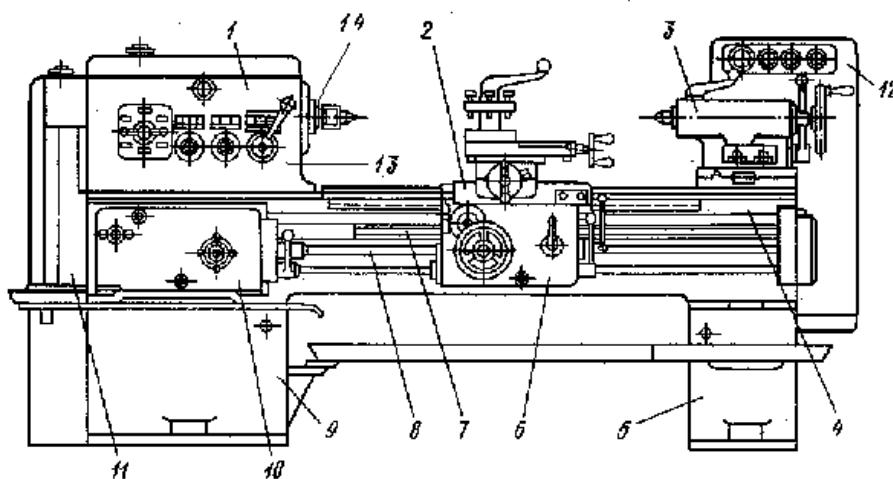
Сборочные единицы (узлы) и механизмы токарно-винторезного станка:
